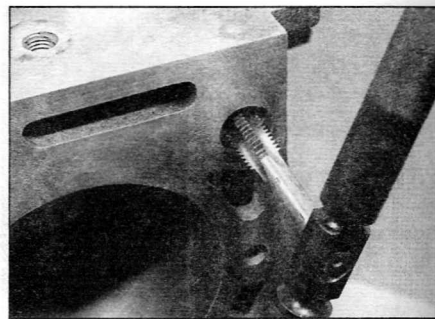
Используйте подходящий метчик для очистки резьбовых отверстий в блоке цилиндров
